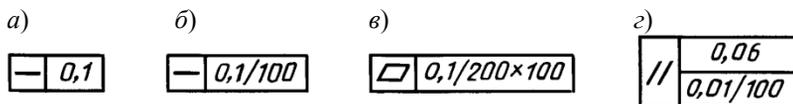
Обозначение допуска по всей длине поверхности
